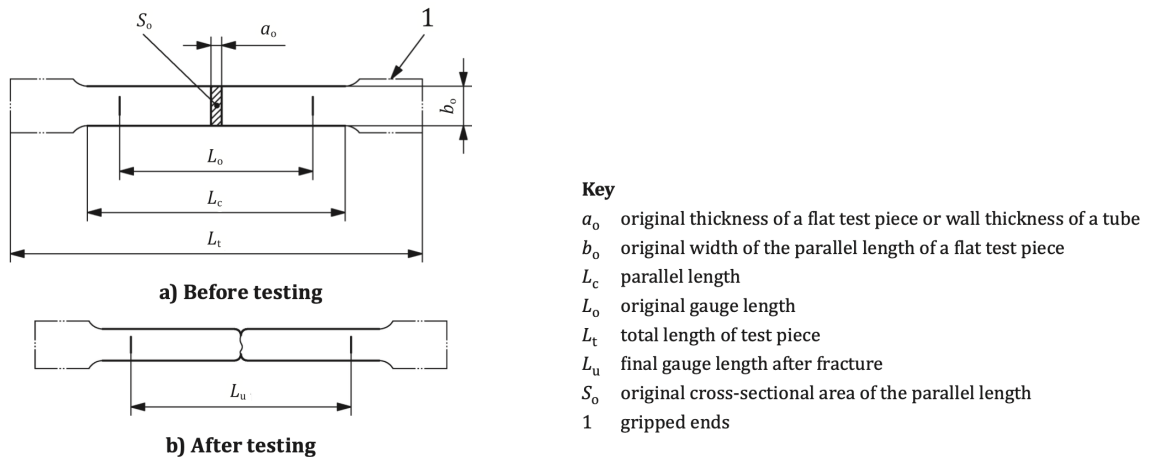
Campione ad "osso di cane" da sezione rettangolare e legenda simboli
